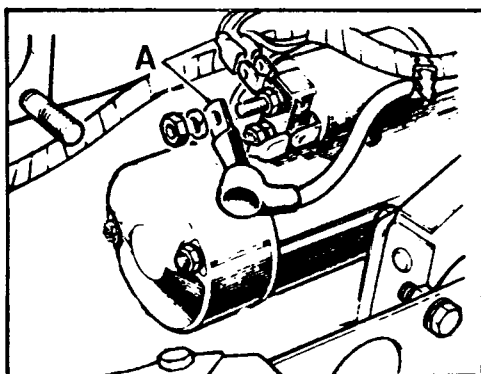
Desmontaje de los cables de alimentación del motor de arranque
